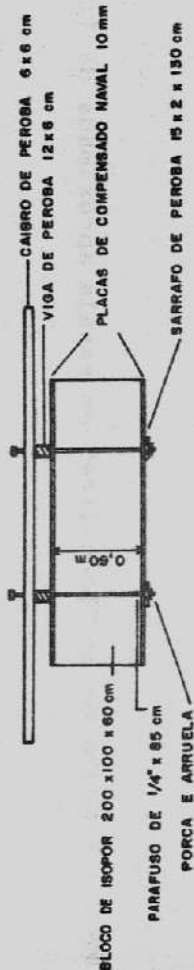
Vista frontal da balsa de crescimento (3 x 6m).
